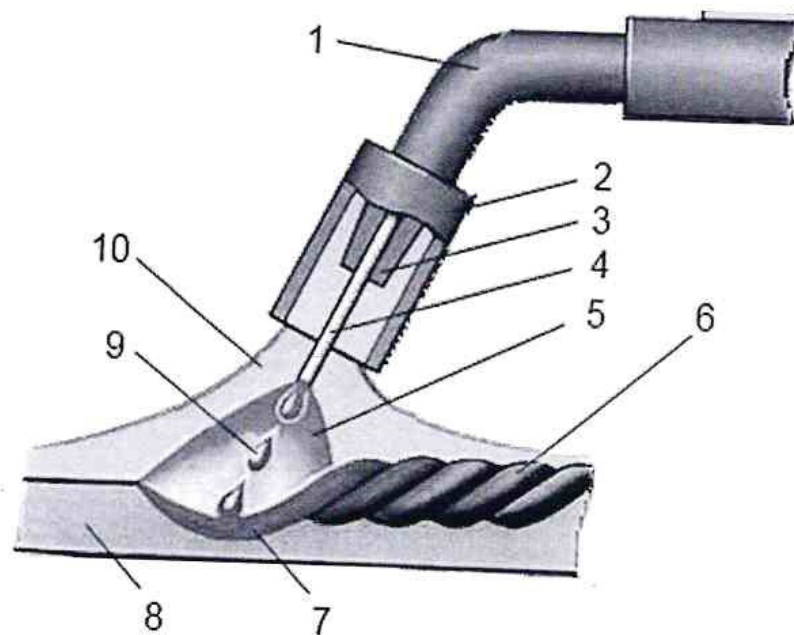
Схема полуавтоматической сварки (MIG/MAG).
